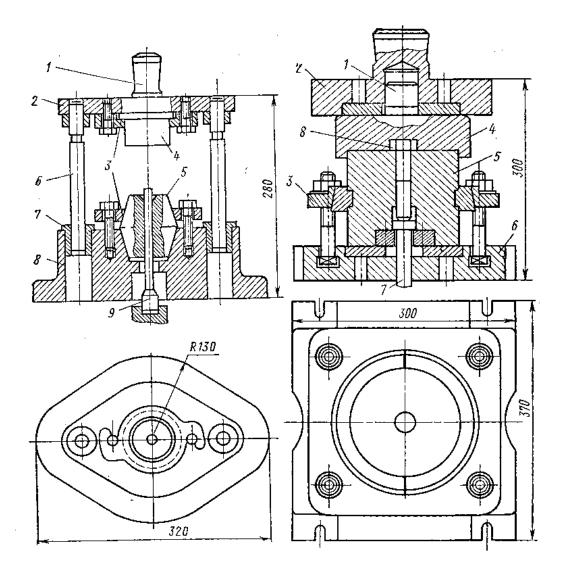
Схема штампа винтового пресс-молота для открытой высадки поковок стержневого типа:
